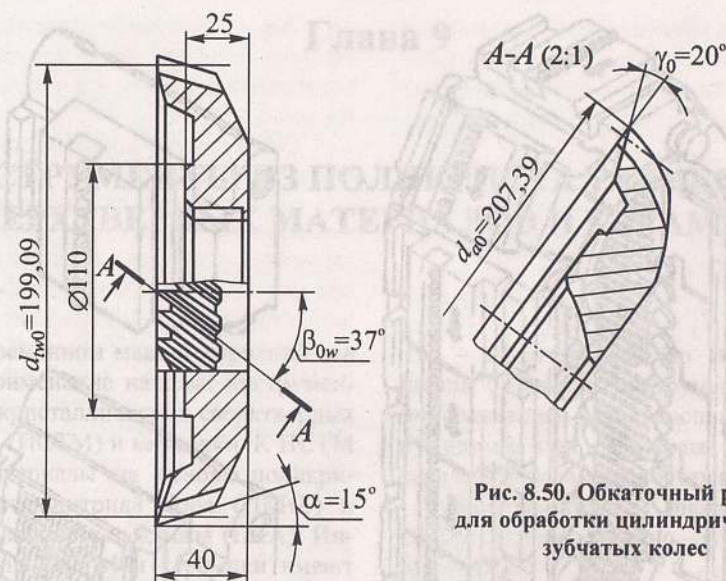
Обкаточный резец для обработки цилиндрических зубчатых колес
